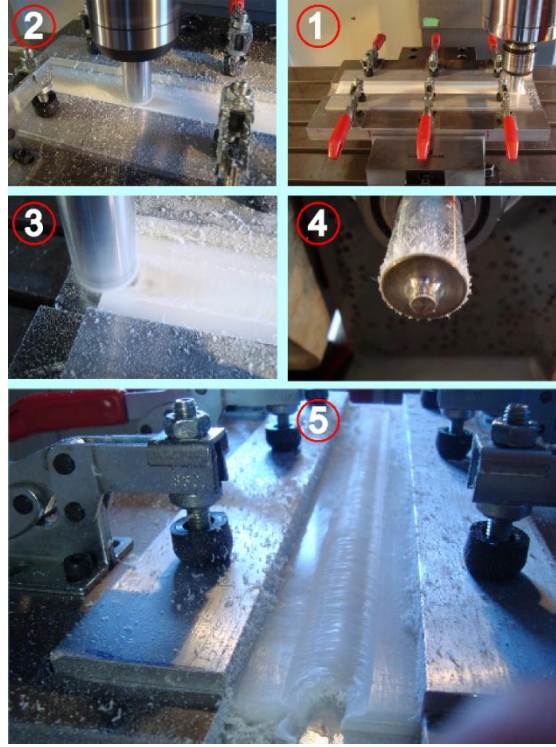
Nelson tarafından geliştirilen SKK kaynak takımı [9]
